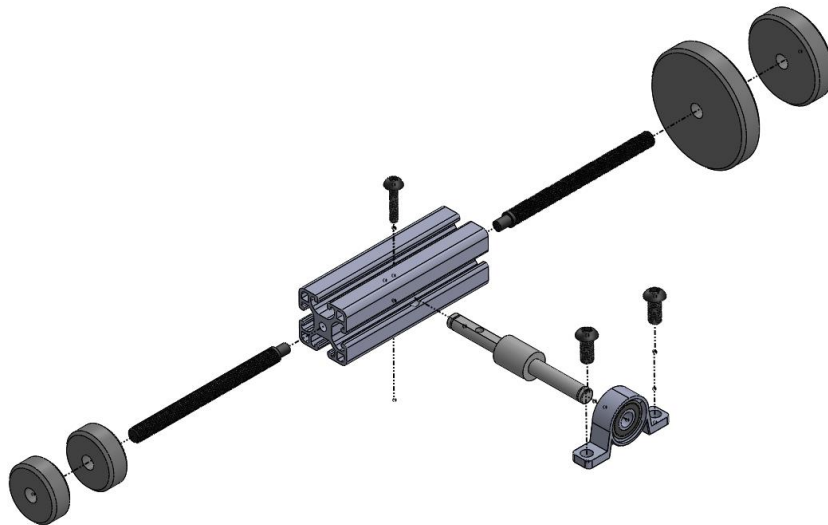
Explosionado sistema de apoyo del brazo conector de la muestra.
